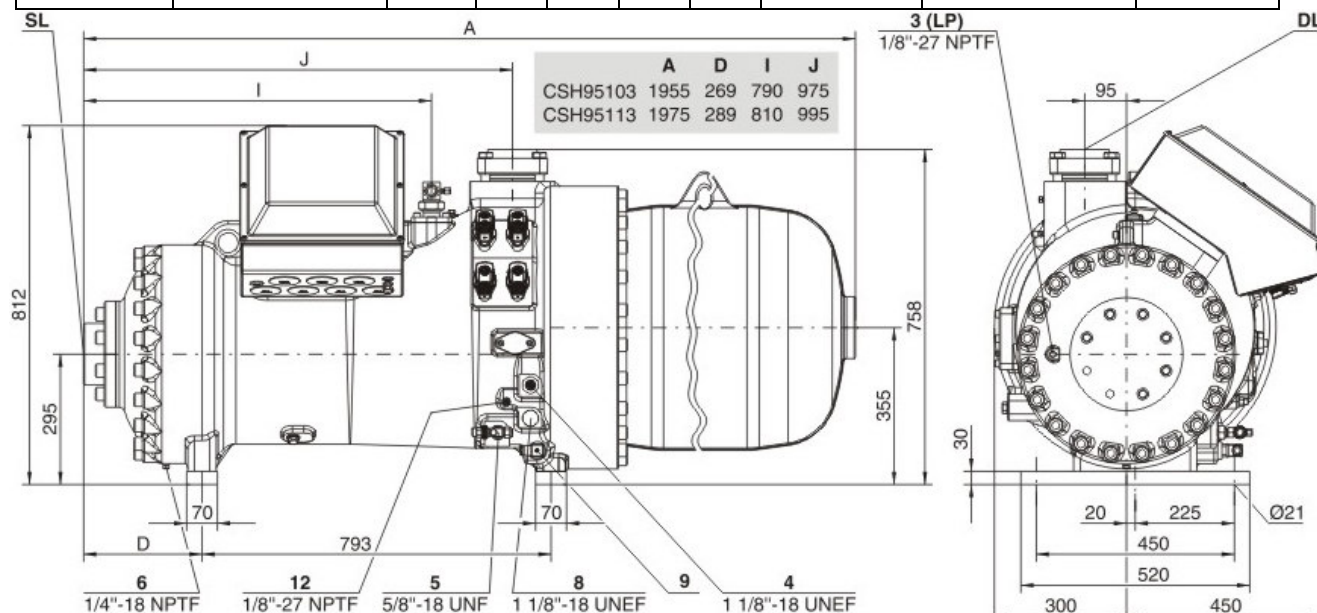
Загальний вигляд компресора Bitzer CSH95113-320Y
